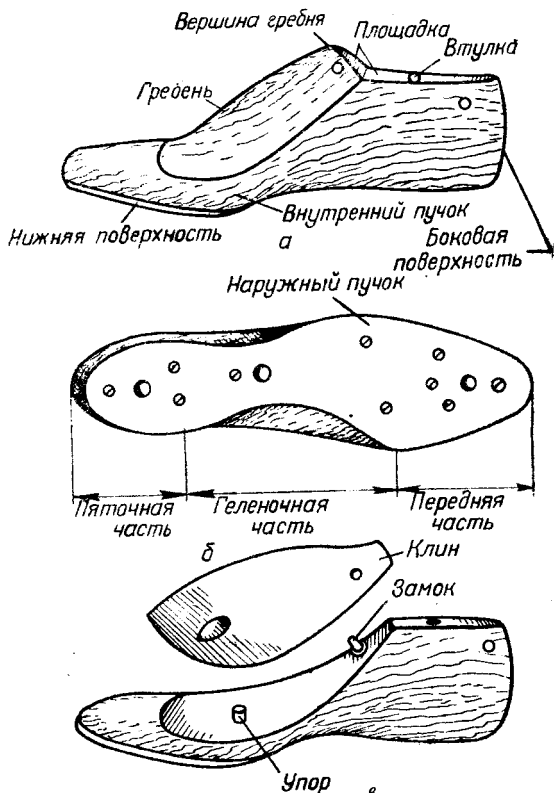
Колодка для глухой затяжки: а — вид сбоку; б — вид со стороны следа; в — со снятым клином
